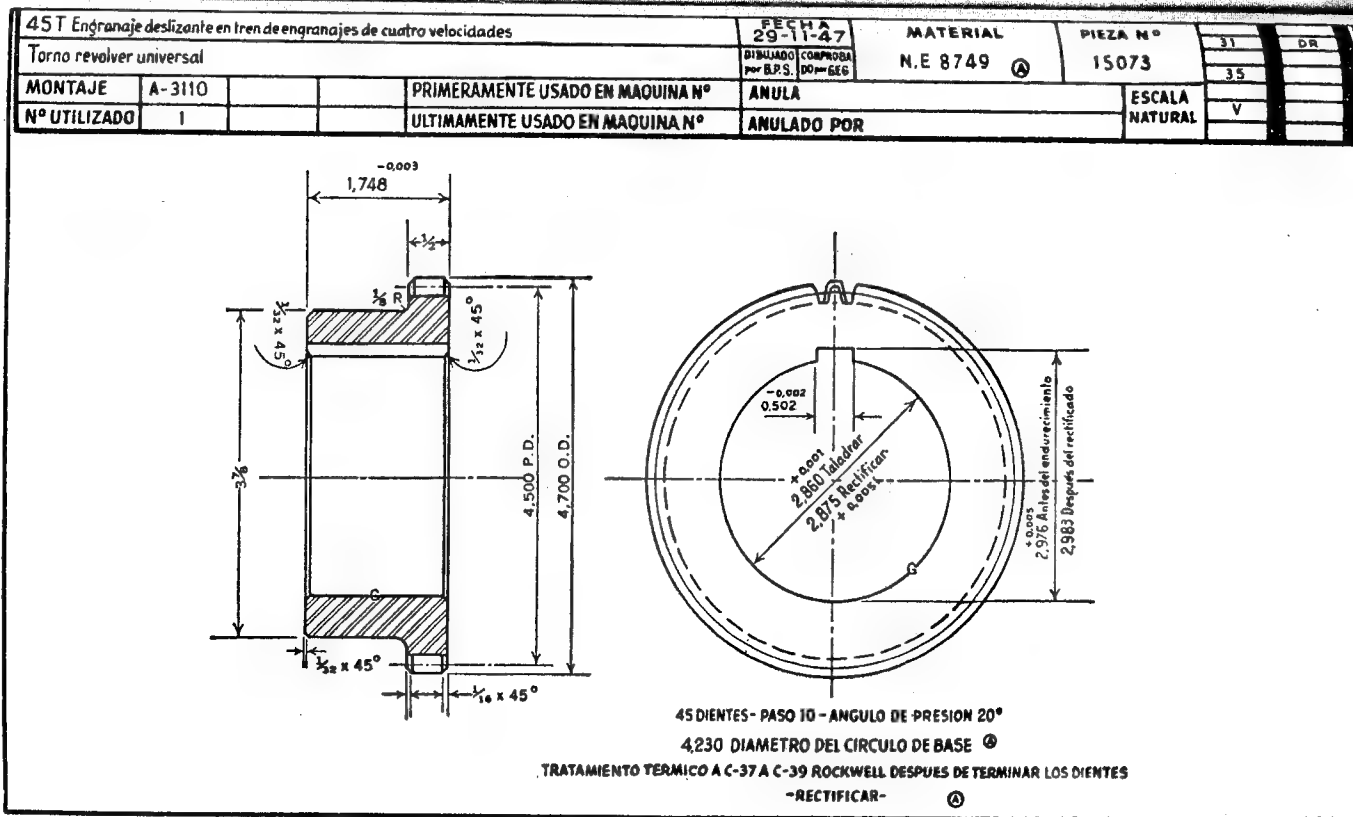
Dibujo detallado de engranaje deslizante, pieza núm. 15073.
